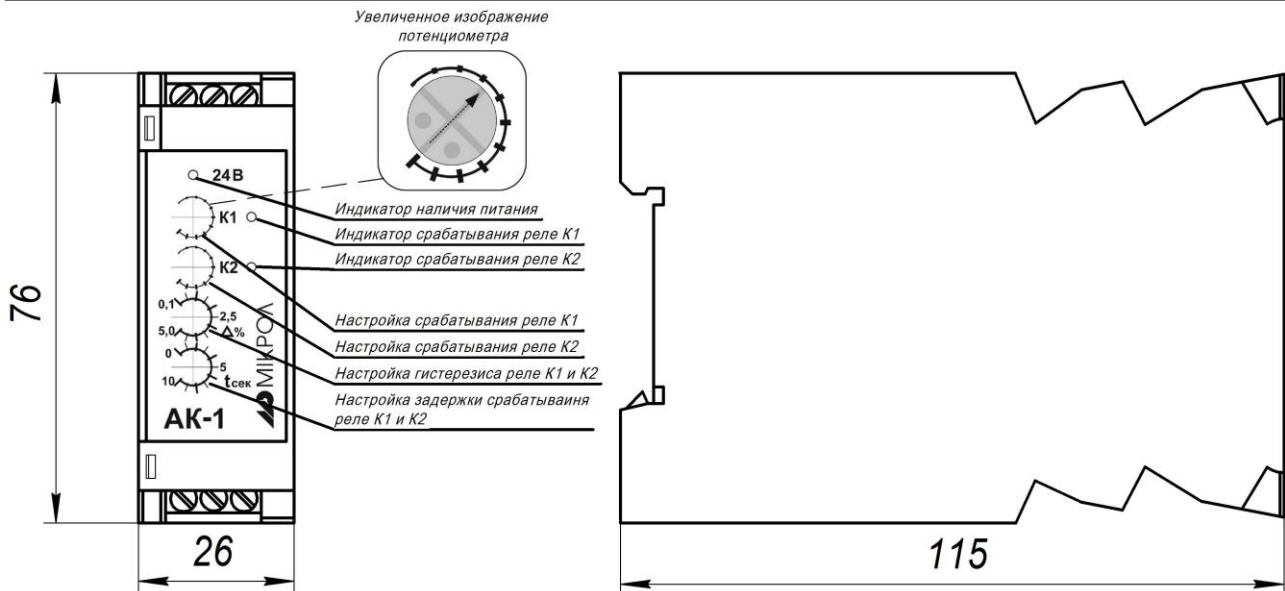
Внешний вид и габаритные размеры АК-1
